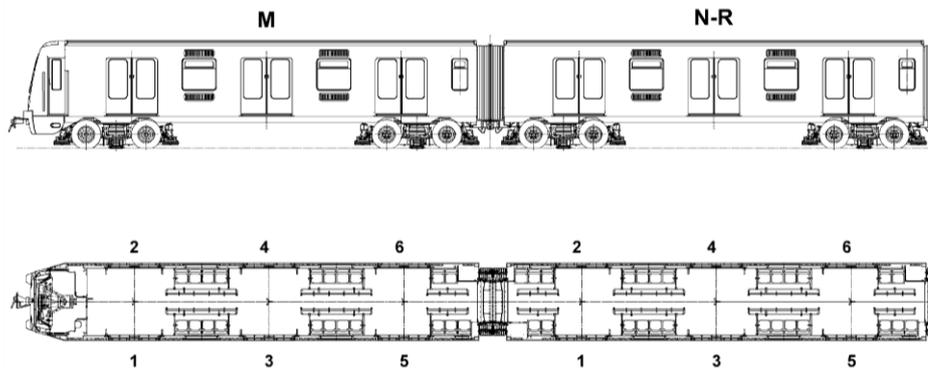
Disposición de las puertas de acceso pasajeros.
